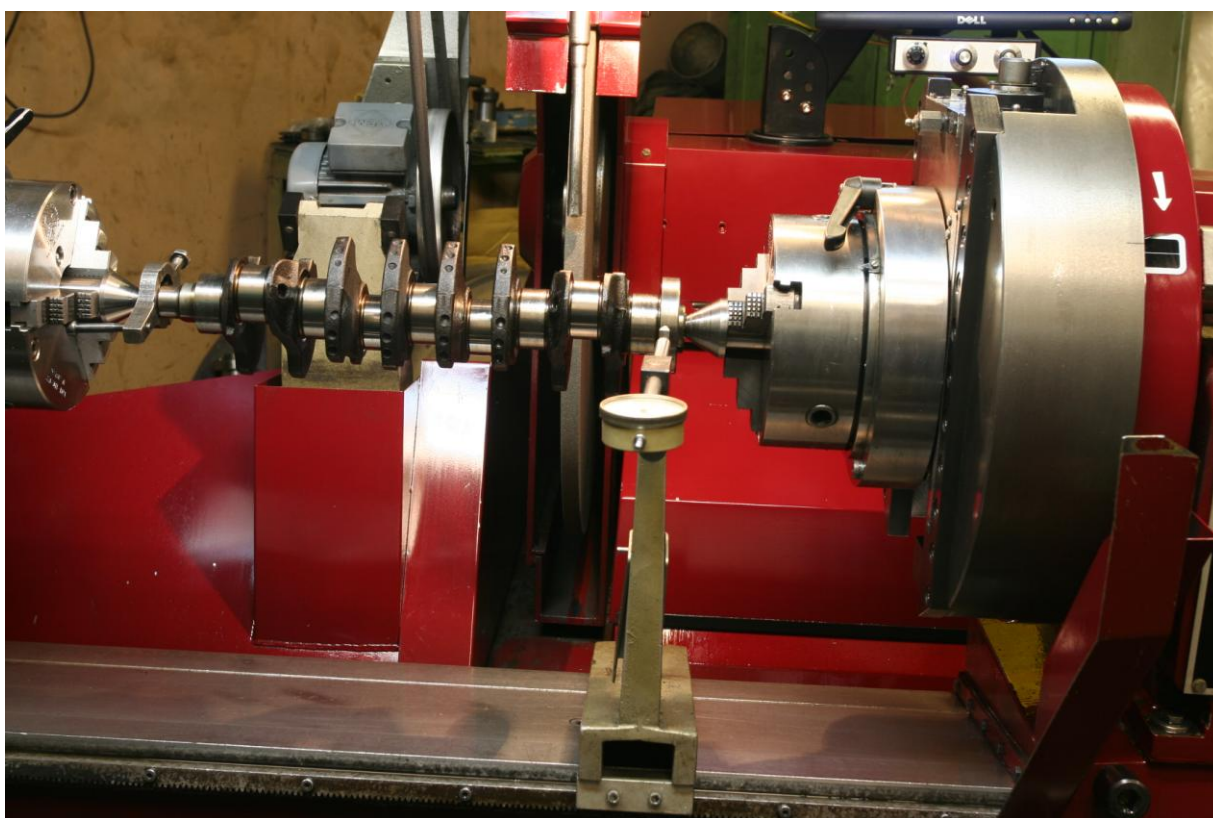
Установить центроискатель на задний фланец вала и повторить проверку. При наличии значительного биения (более 0,02 мм) необходимо снять вал со станка и поправить центровые фаски вала.
